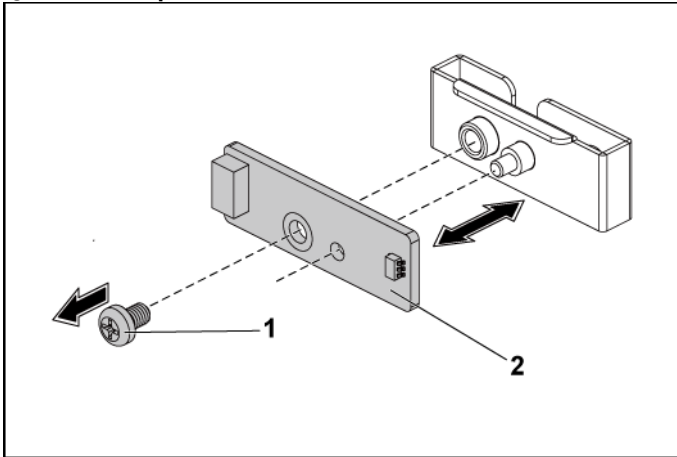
Sensorplattenbaugruppe entfernen und installieren
